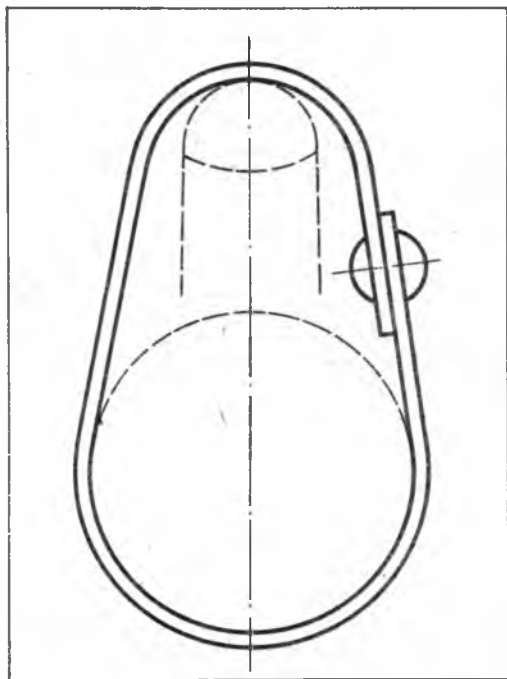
Кольцо, надеваемое на рукоятку стояночного тормоза, и рычаг декомпрессора при пуске двигателя
